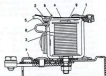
Interruttore di minima del gruppo A-400/1.
